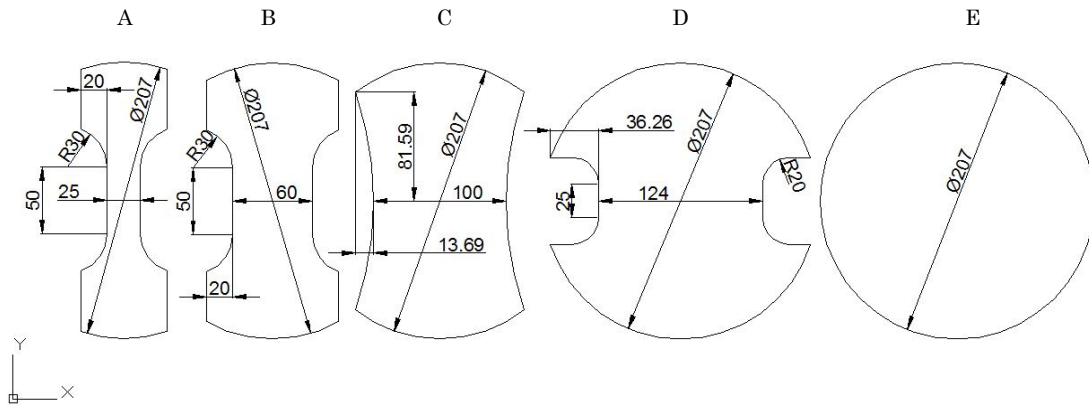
Detalle de las geometrías de las probetas de Inconel 718 para el ensayo Nakajima
